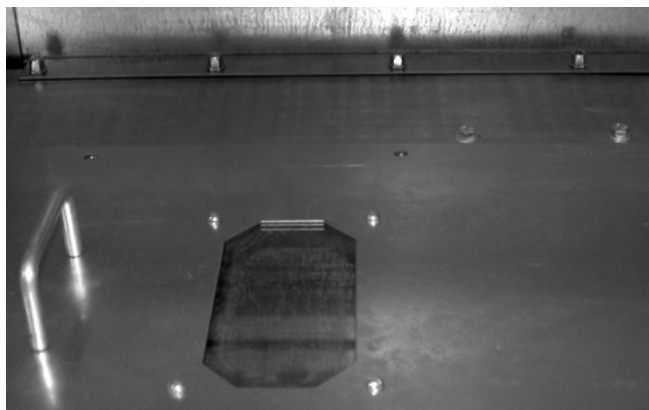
Съемные перегородки со смотровыми окнами в отсеке сборных шин
